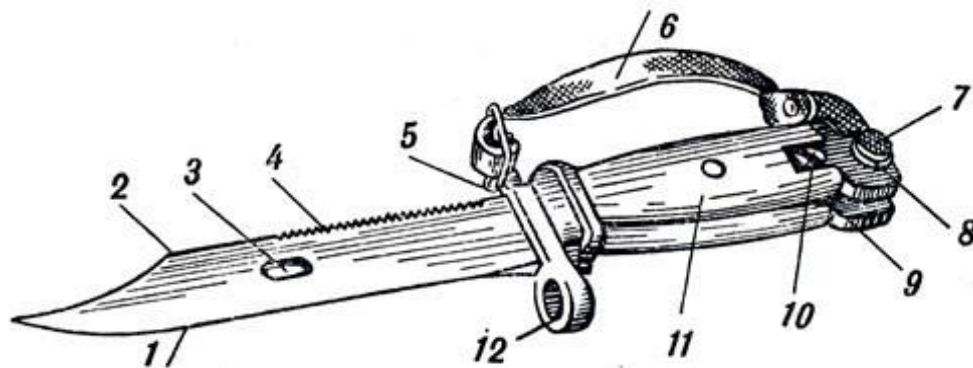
Штык-нож: 1 — лезвие; 2 — режущая кромка; 3 — отверстие; 4 — пила; 5 — зацеп; 6 — ремень; 7 — защелка; 8 — предохранительный выступ; 9 — продольный паз; 10 — винт наконечника; 11 — рукоятка; 12 — кольцо
